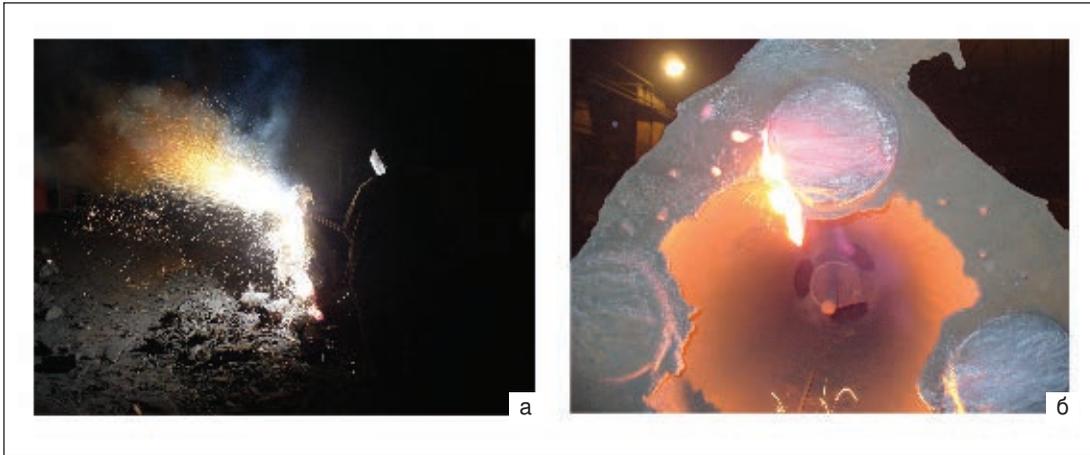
Резка прибыли из стали 40Х9С2Л диаметром 270 мм (а) и поверхность реза (б)
